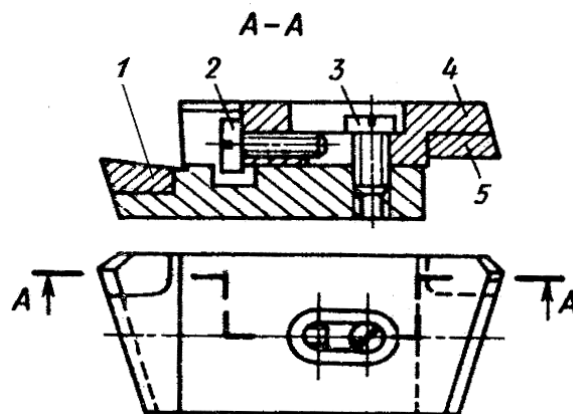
Плаваючий дволезовий блок з напаяними пластинками з твердого сплаву
